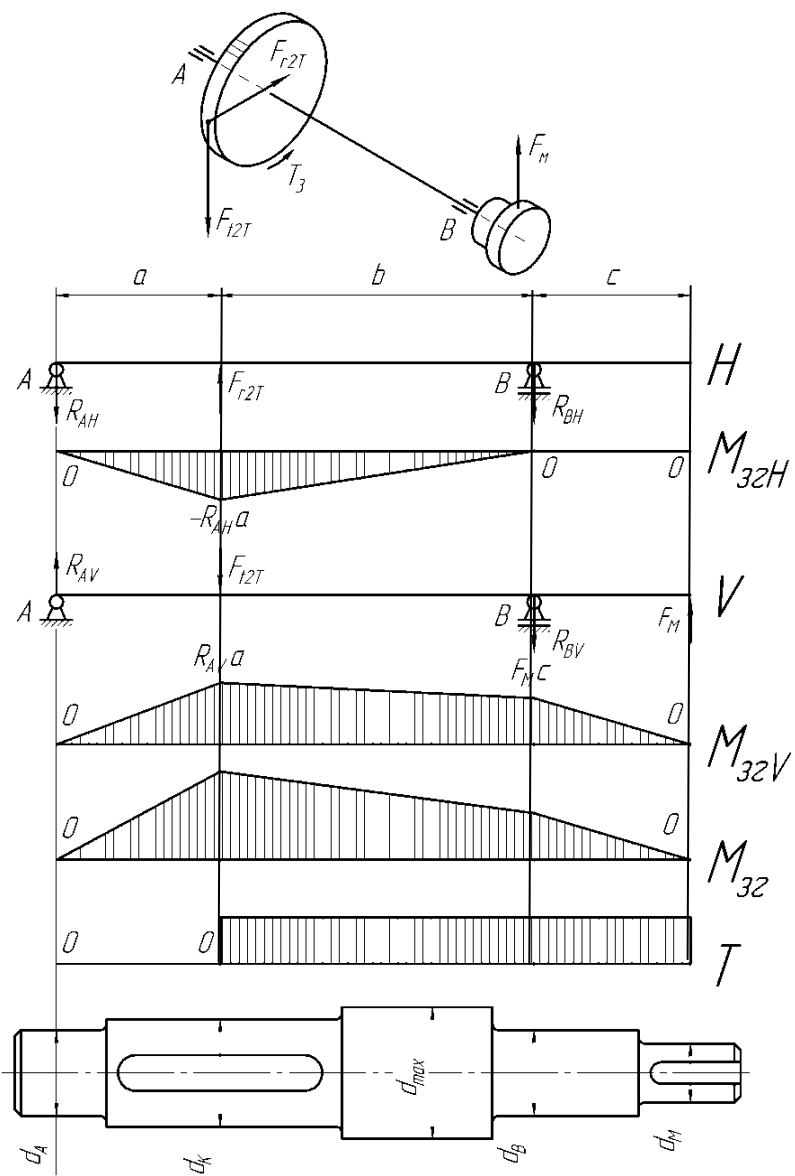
Розрахункова схема, епюри моментів і ескіз веденого вала циліндричного двоступінчастого редуктора
